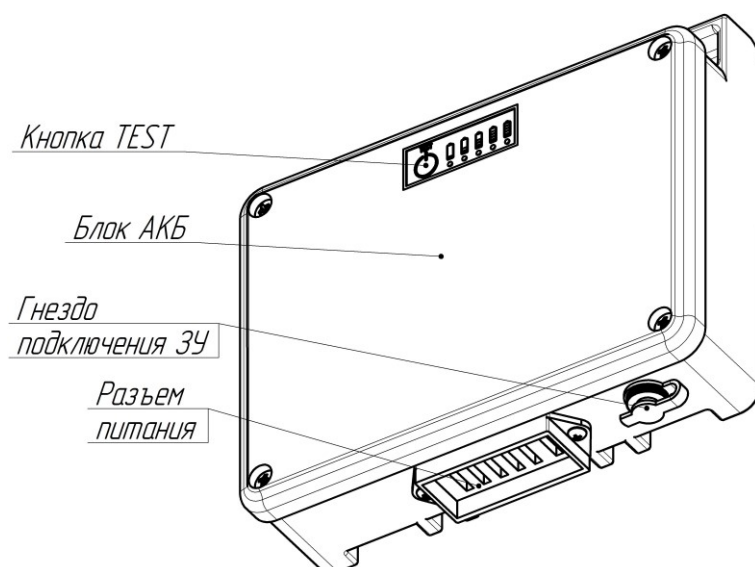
Внешний вид блока АКБ (вид снизу)
